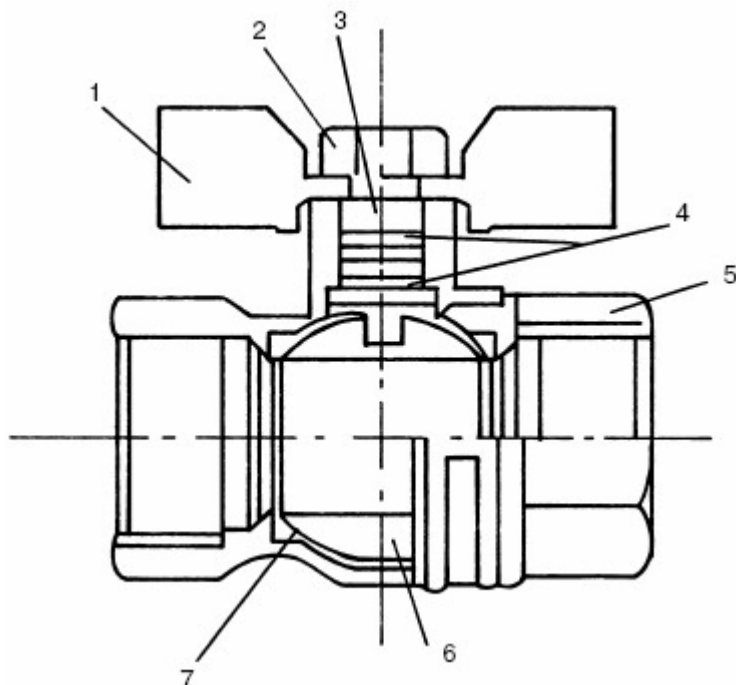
Шаровой кран: 1 – ручка; 2 – гайка, фиксирующая ручку на штоке; 3 – шток; 4 – уплотнительные кольца; 5 – корпус клапана; 6 – шаровой затвор; 7 – уплотнительные тефлоновые кольца
